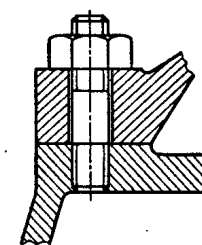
Крепление сборочной единицы к плите шпильками
